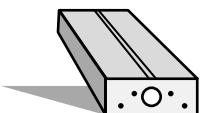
Lage der Bohrungen in der Moduleseitenwand zur Befestigung frei verwendbarer ModulfüÙe oder auch für passendes modulfremdes Zubehör. Die Maße beziehen sich auf die Standardabmessungen der Kopfstücke gemäß Abb. 1.1 und 1.2.
